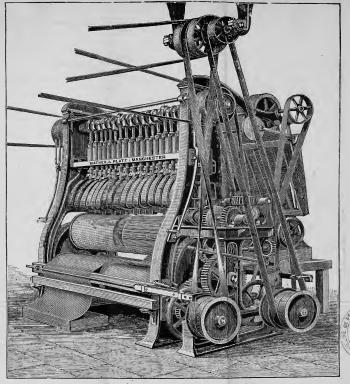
Machine à bettler, construction Mather et Platt, de Manchester.
